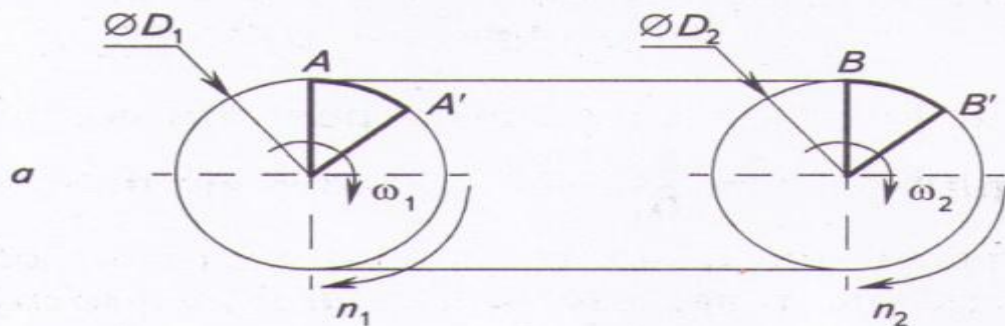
Механизм передачи движения в токарном станке по обработке древесины
